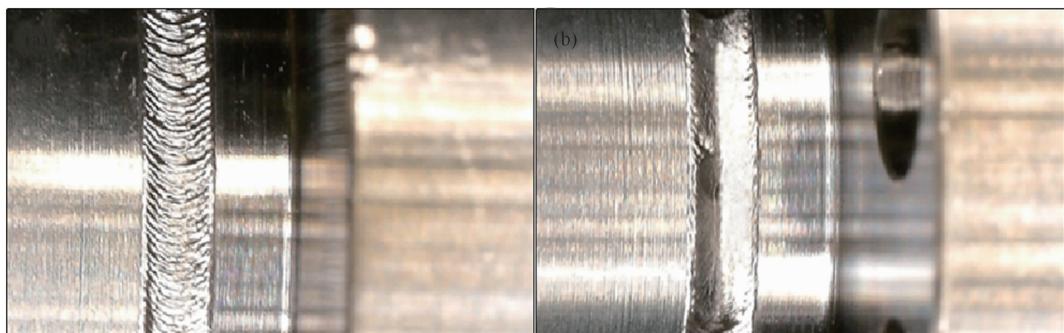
焊缝表面形貌的宏观对比: (a) 激光抛光前; (b) 激光抛光后
